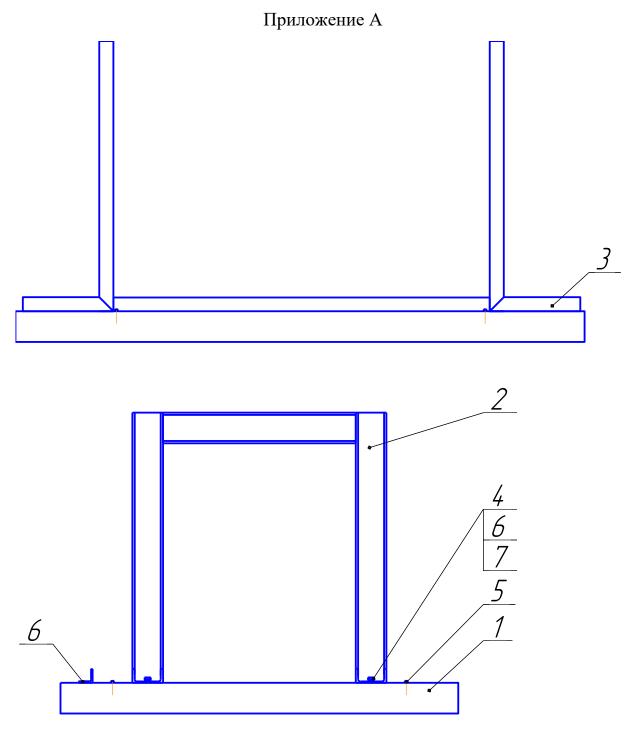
Устройство приспособления сборочно-сварочного $\Phi \mbox{OPA.000001.161.00.000 CF}$
